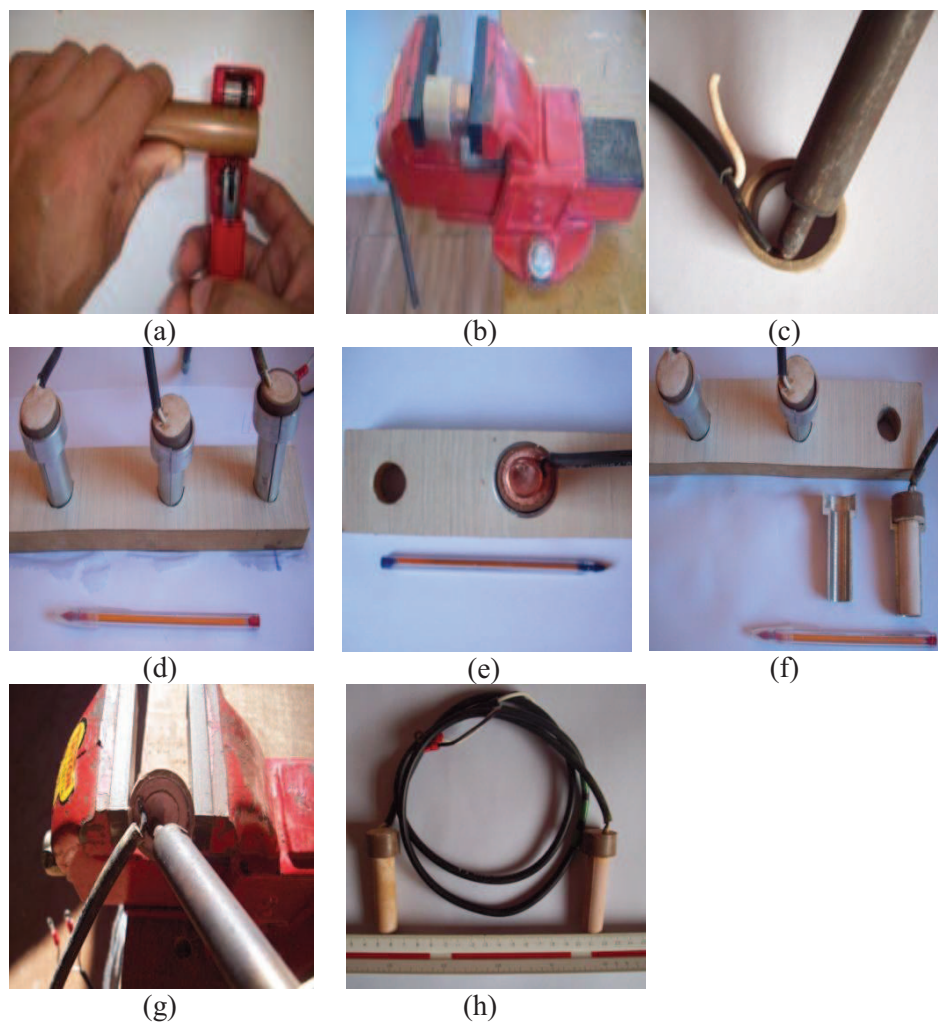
Etapas da construção do DC: corte do tubo de cobre (a), inserção do eletrodo externo (b), soldagem de fio no eletrodo externo (c), preenchimento das formas (d), inserção do eletrodo interno (e), período de secagem (f), soldagem de cabo PP - eletrodo interno (g), capacitores cilíndricos (h)
